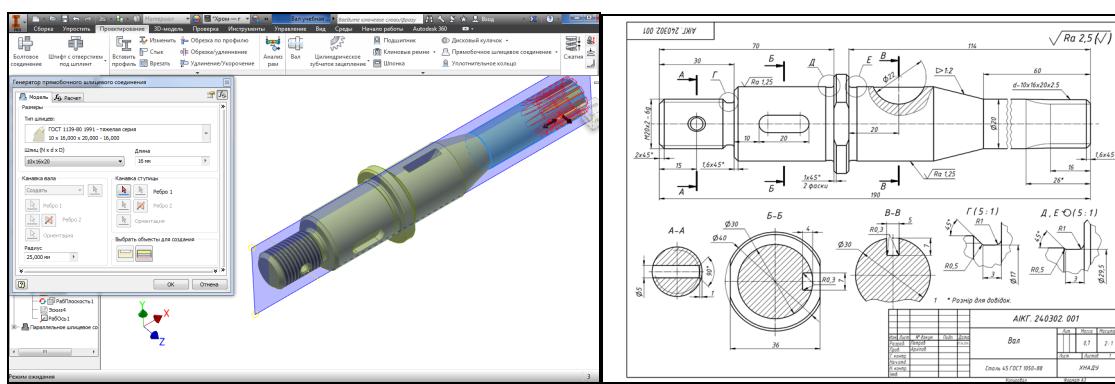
Модель та робочий кресленик деталі "Вал шліцьовий".
